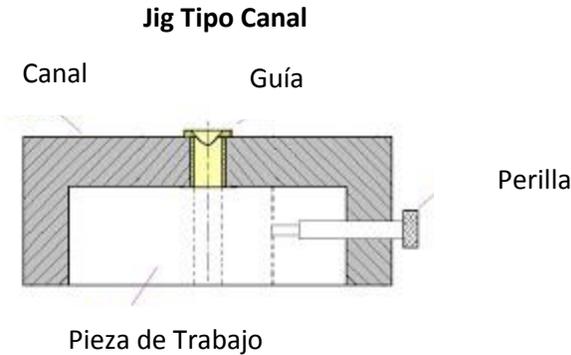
Jig tipo canal. Fuente American Machinist
